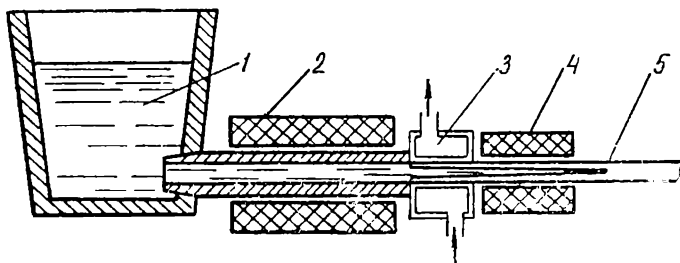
Расположение электромагнитных устройств в установке непрерывной разливки металла:
